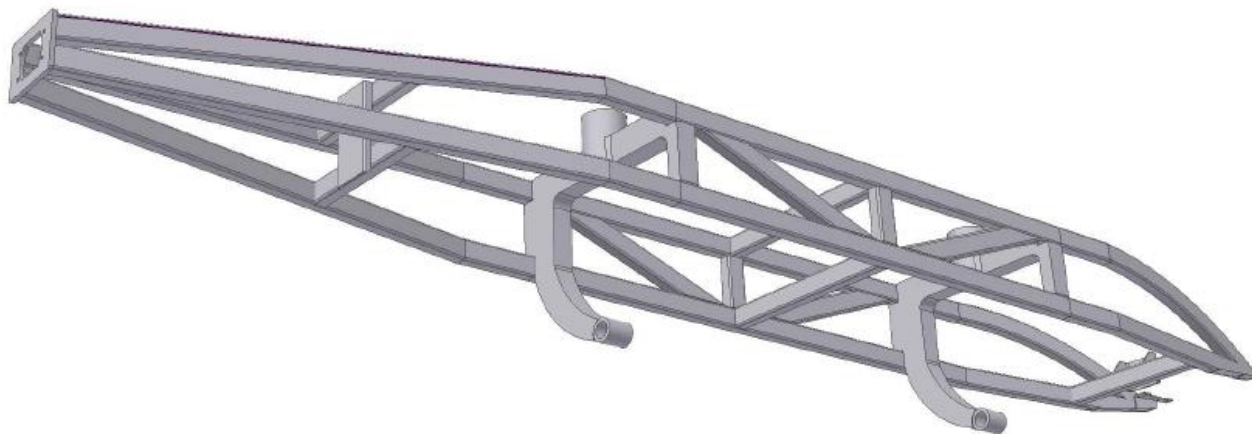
Каркас сварной шасси моно-юнибуса Ю-373П
